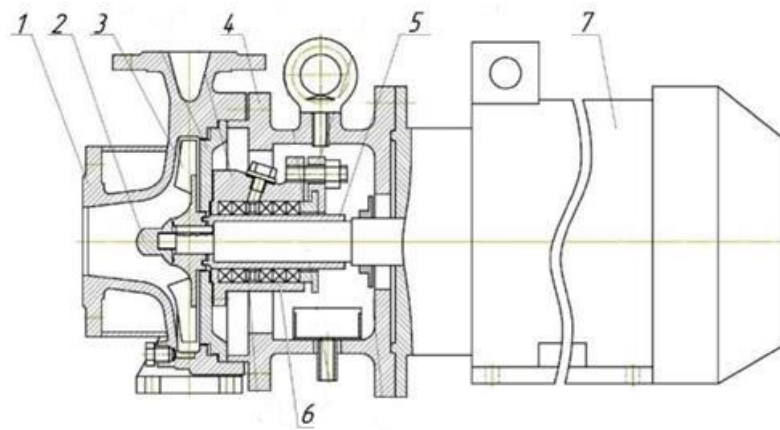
Схема центробежного насоса моноблочного типа 1XM–2–2В: 1 – корпус насоса; 2 – гайка рабочего колеса; 3 – рабочее колесо; 4 – промежуточный фонарь; 5 – удлинитель; 6 – сальниковое уплотнение; 7 – электродвигатель [30].
